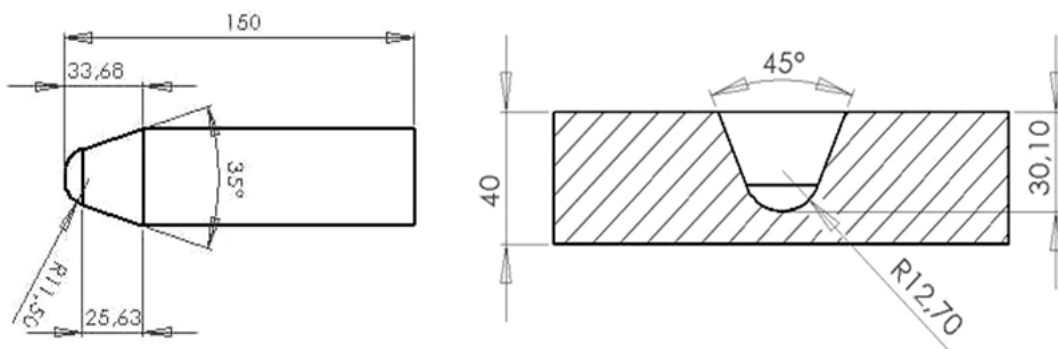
Dimensões para fabricação dos corpos de prova.
